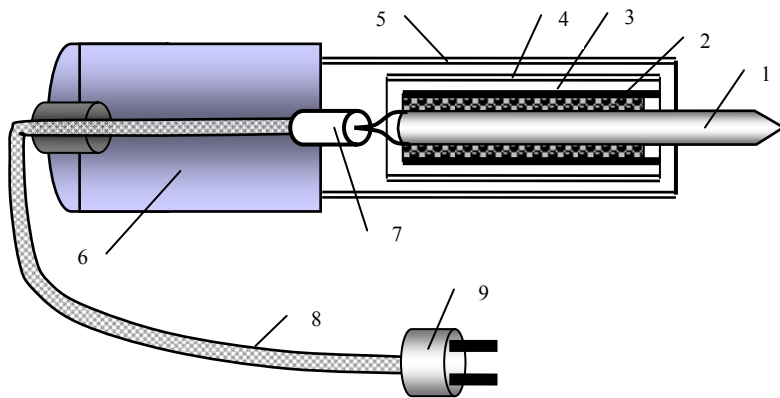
Схема электропаяльника: 1 – стержень; 2 – нагревательный элемент; 3 – прокладка; 4 – кожух; 5 – трубка; 6 – ручка; 7 – изолятор; 8 – кабель; 9 – вилка
